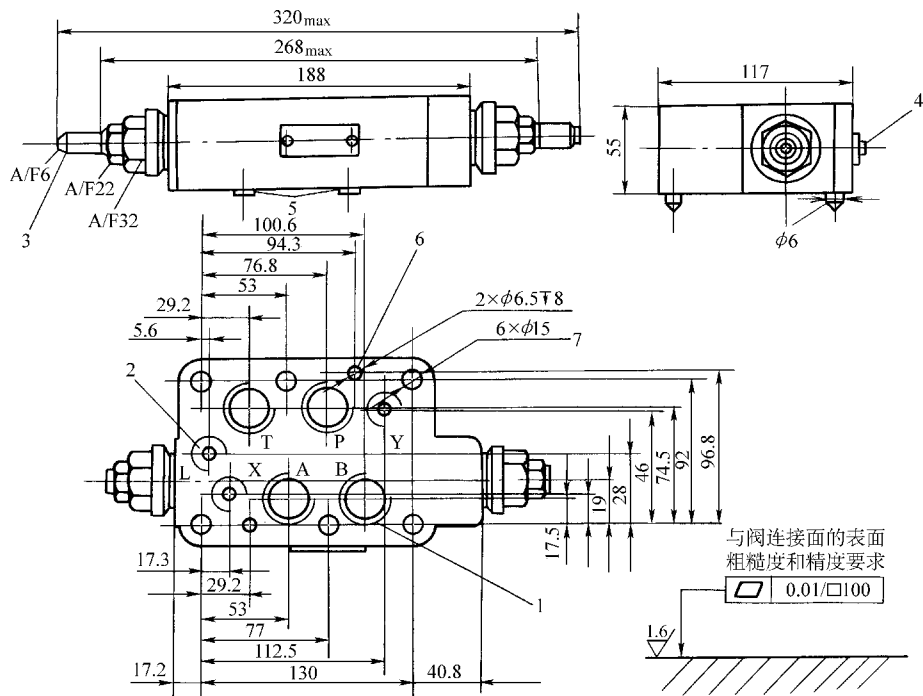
Z2FS22 型叠加式节流阀的外形尺寸
